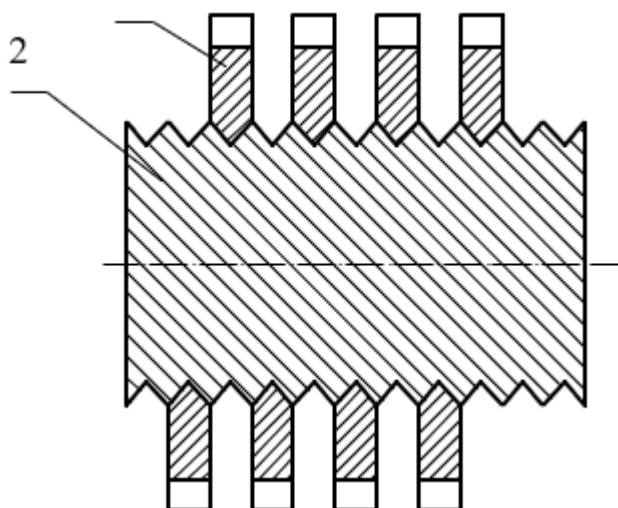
Конструктивне виконання гайки, сформованої зі стрічкової навивної заготовки.
